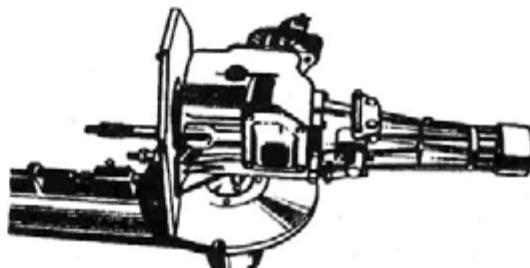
Стенд с поворотным устройством для разборки сборки коробки передач
